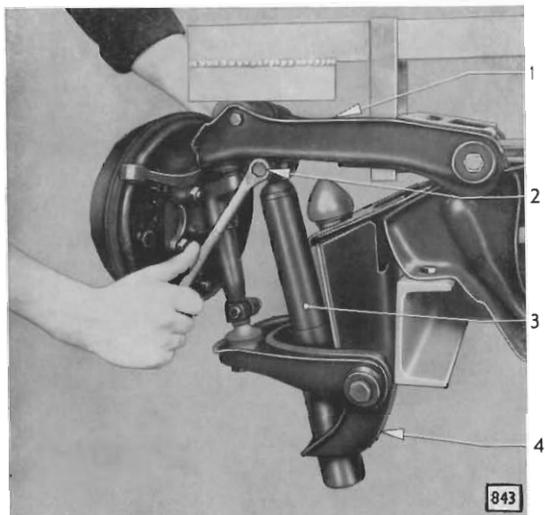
Sechskantschraube für Befestigung Stoßdämpfer am unteren Lenker abschrauben
